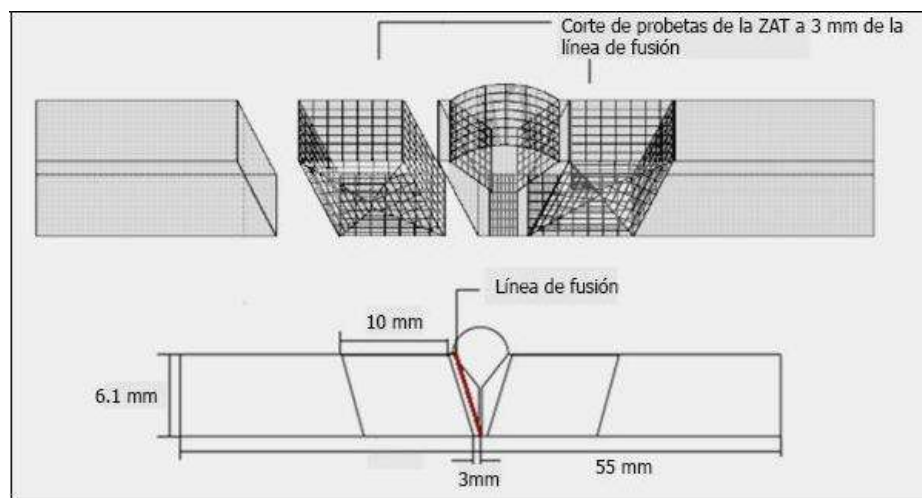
6. Representación del corte de probetas de la ZAT a 3 mm de la línea de fusión de los cordones de soldadura.
